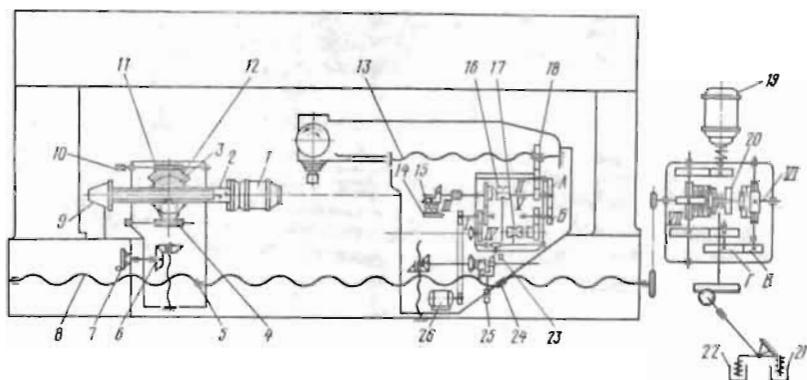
Кинематическая схема станка ФОЛ-2М
